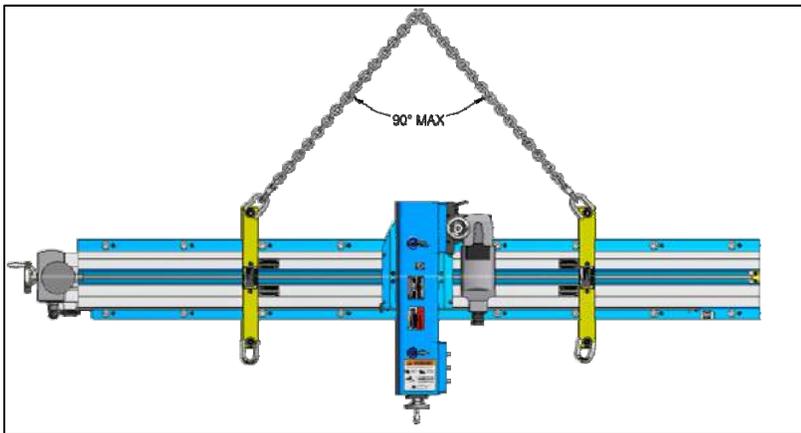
LEVAGE VERTICAL - HORIZONTAL
